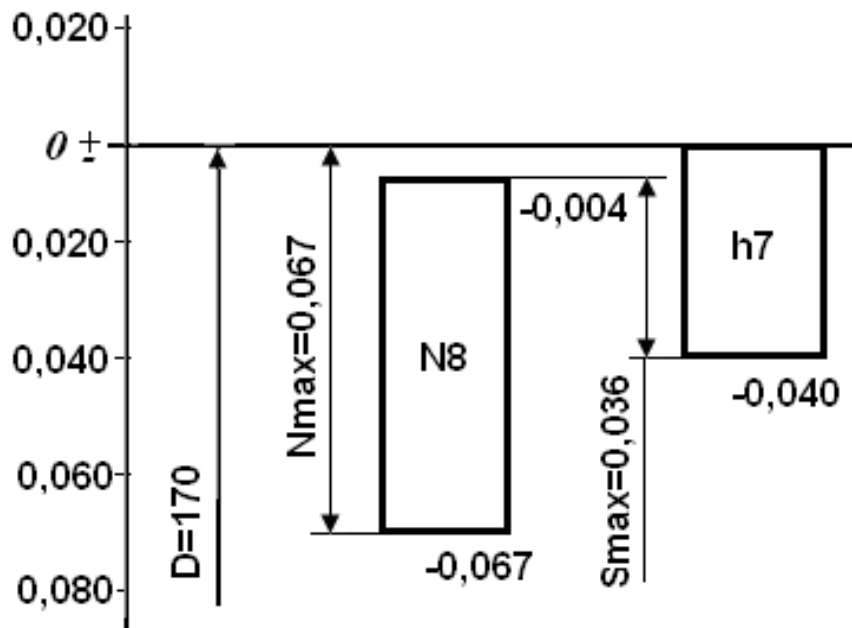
Схема розташування полів допусків деталей з'єднання $\varnothing 170N8/h7$
